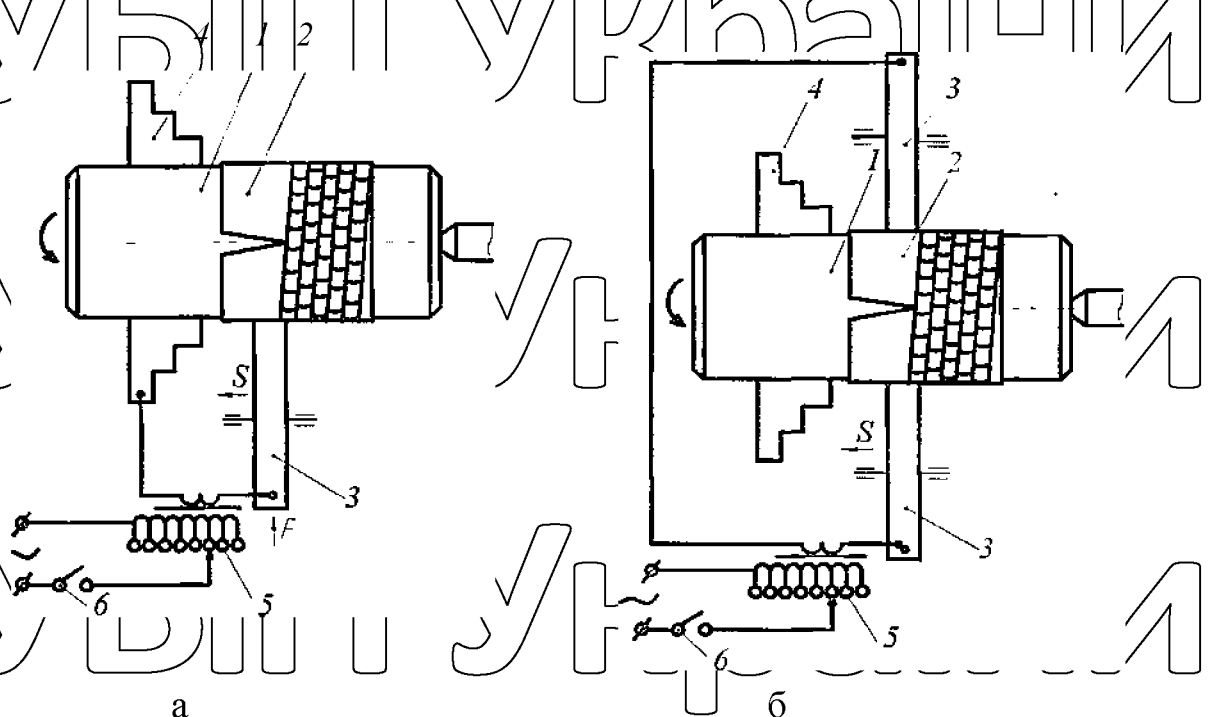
Схеми відновлення валів електроконтактним приварюванням сталевих стрічок: а – однороликова схема наплавлення; б – двороликова схема (1 – відновлювана деталь; 2 – присадкова стрічка; 3 – ролик-електрод; 4 – патрон; 5 – зварювальний трансформатор).
